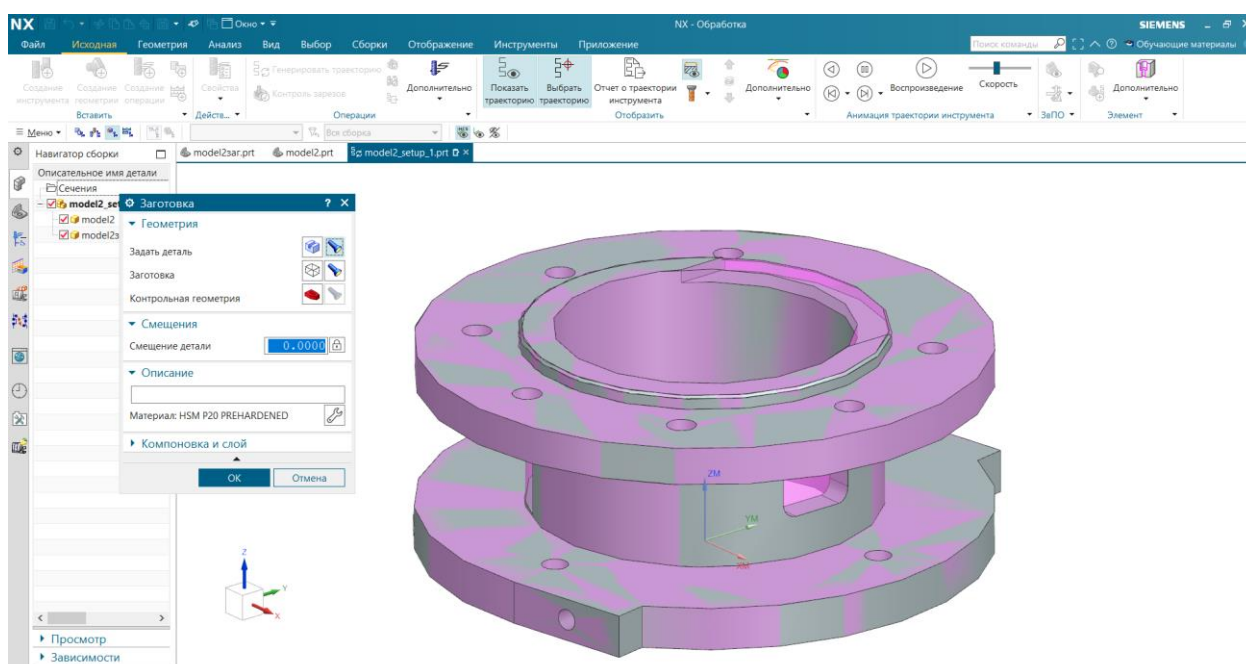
Визначення деталі, заготовки в системі NX CAM
